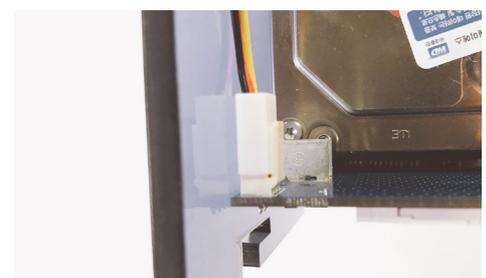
Inserta el cable del ventilador en la placa CloudShell-2
